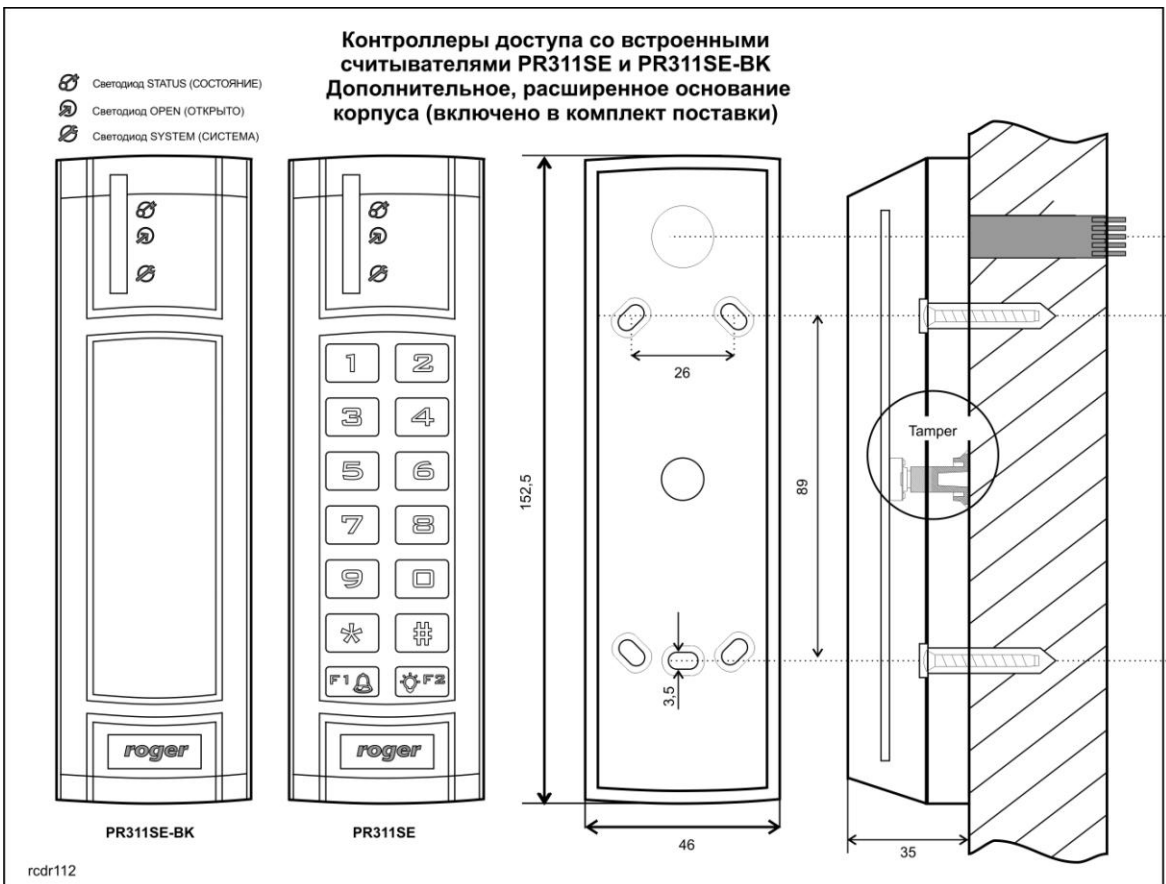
Контроллер PR311SE с дополнительным основанием корпуса
